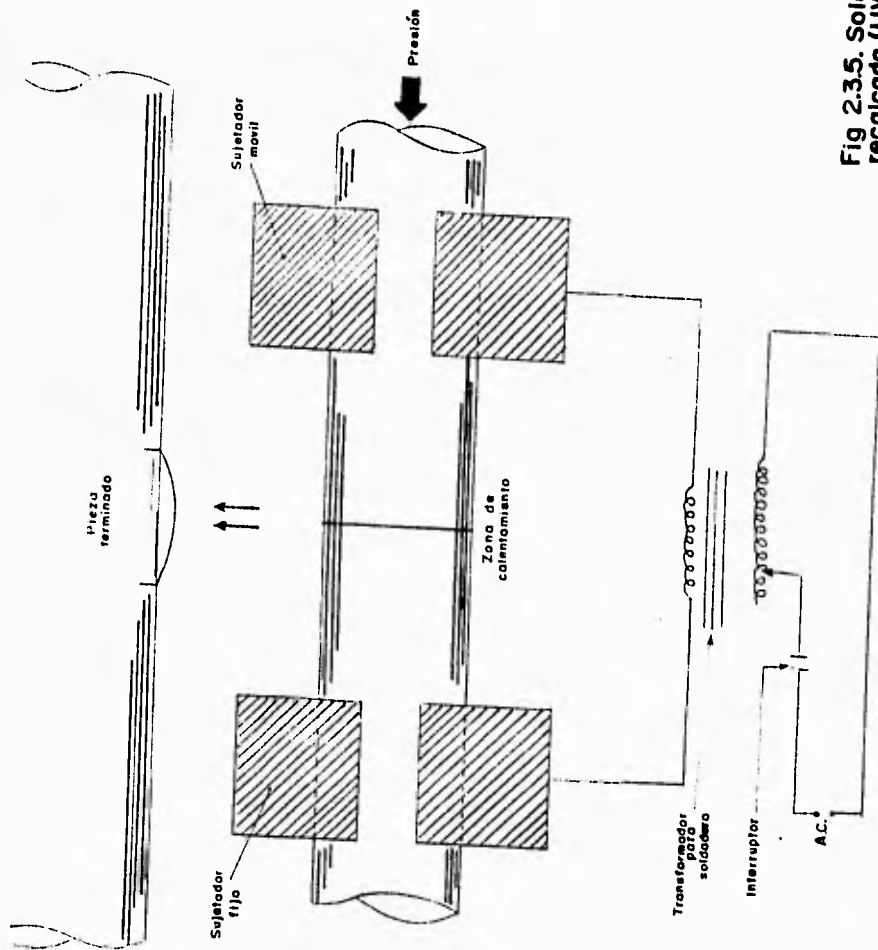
Soldadura recalcada (UW)
